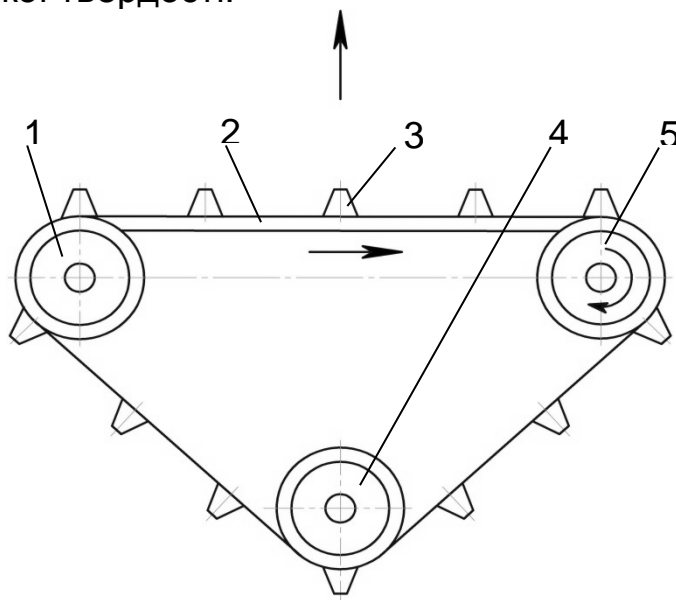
Пасово-сегментний різальний апарат: 1 – ведучий шків; 2 – клиновидний пас; 3 – сегмент; 4 – натяжний шків; 5 – ведучий шків.
